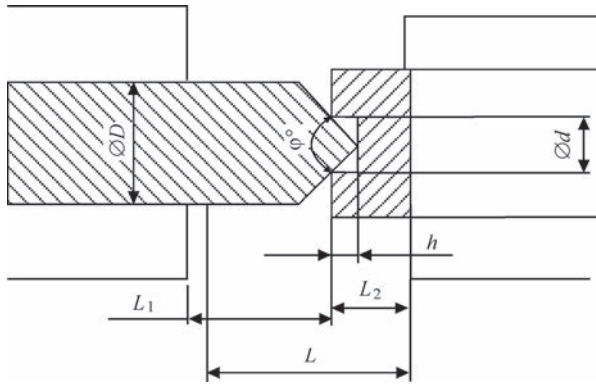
Схема предварительной подготовки свариваемых кромок штока и проушины при КСС сопротивлением
